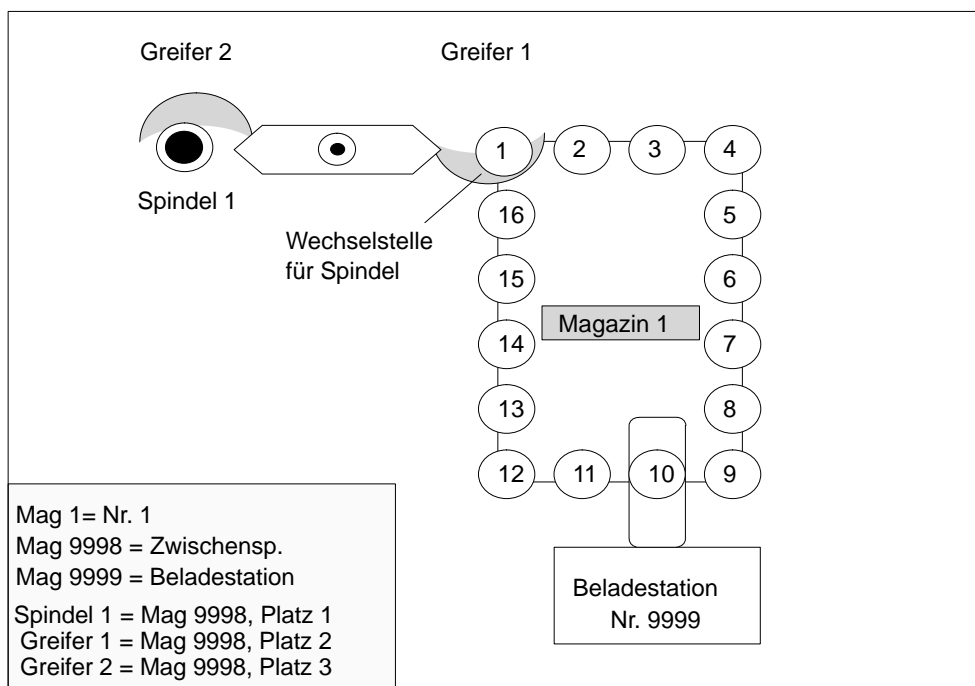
Werkzeugmaschine mit einem Kettenmagazin
